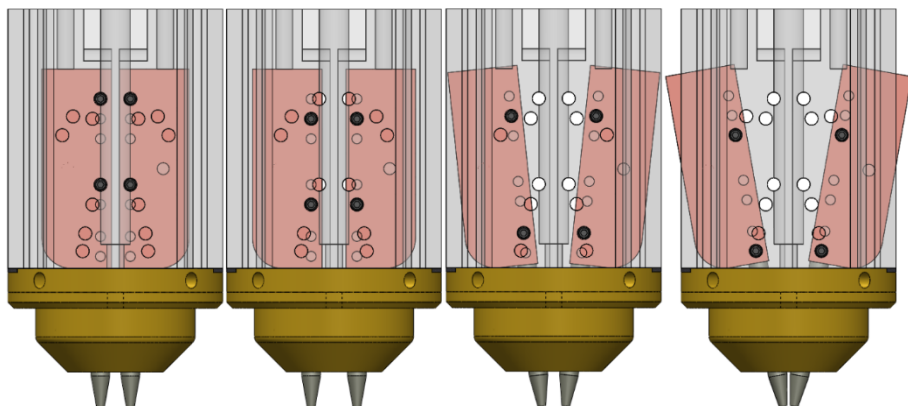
Desenhos esquemáticos mostrando as 4 posições padrão para cada eletrodo na 2ª versão de tocha de soldagem TIG-DE desenvolvida pelo LABSOLDA - UFSC
